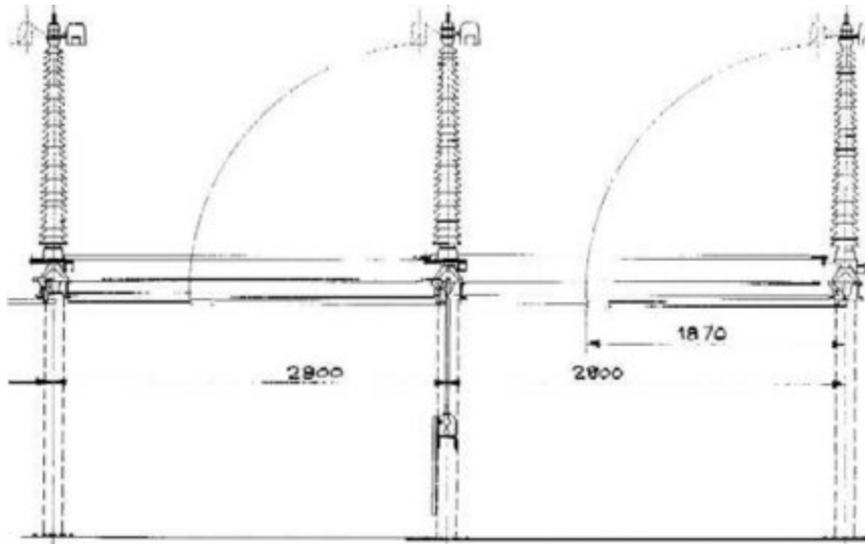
α VISTAS DE UN SECCIONADOR ROTATIVO DE TRES COLUMNAS CON CUCHILLAS DE PUESTA A TIERRA.
